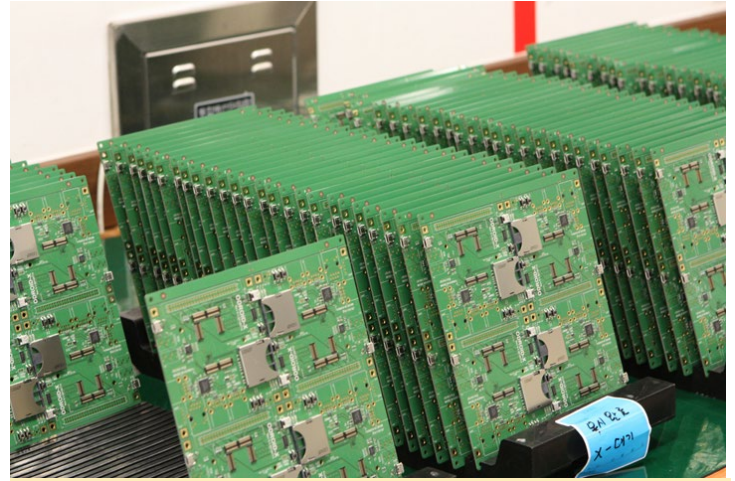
La soldadura SMT está terminada, y las placas están listas para someterlas al proceso de inspección
